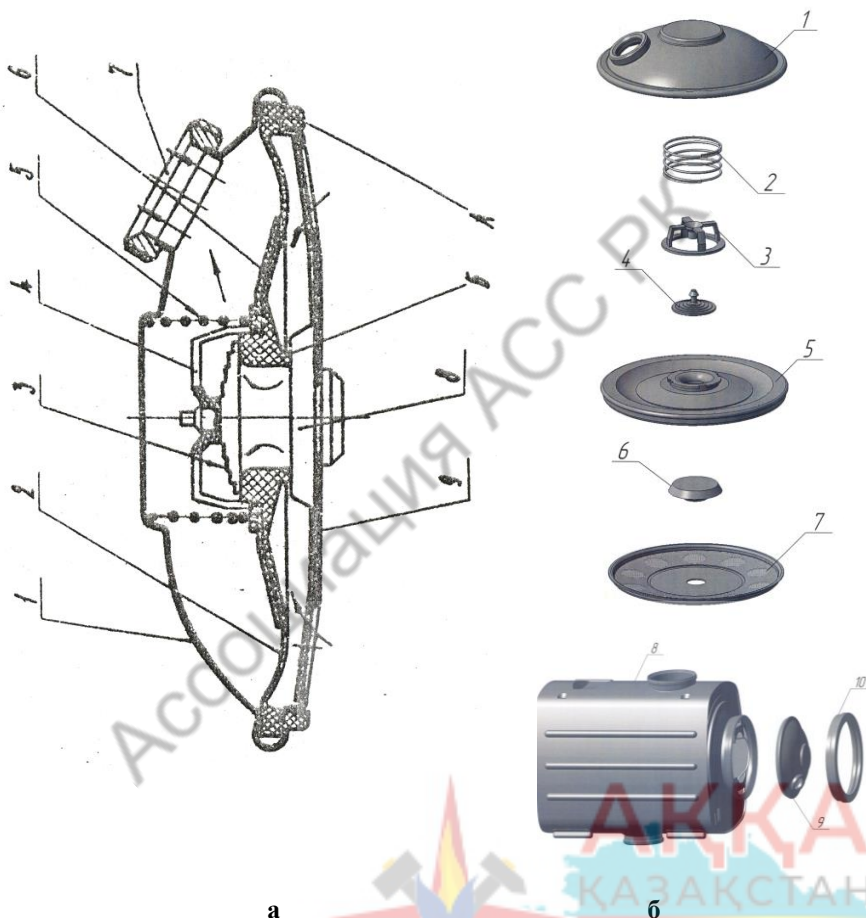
Клапан избыточный респиратора Р-30, патрон регенеративный
